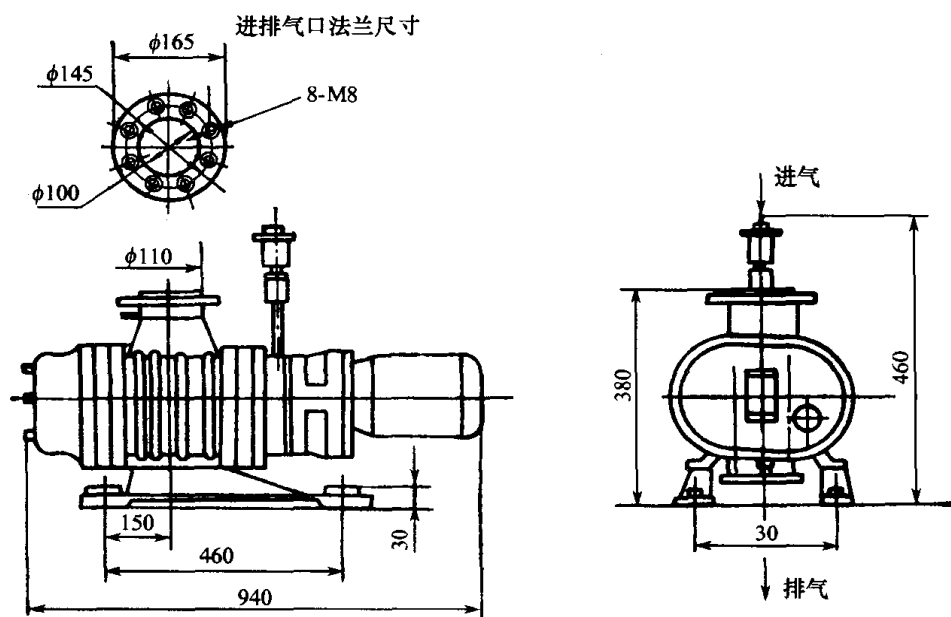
ZJ-150C 型罗茨泵外形及安装尺寸
